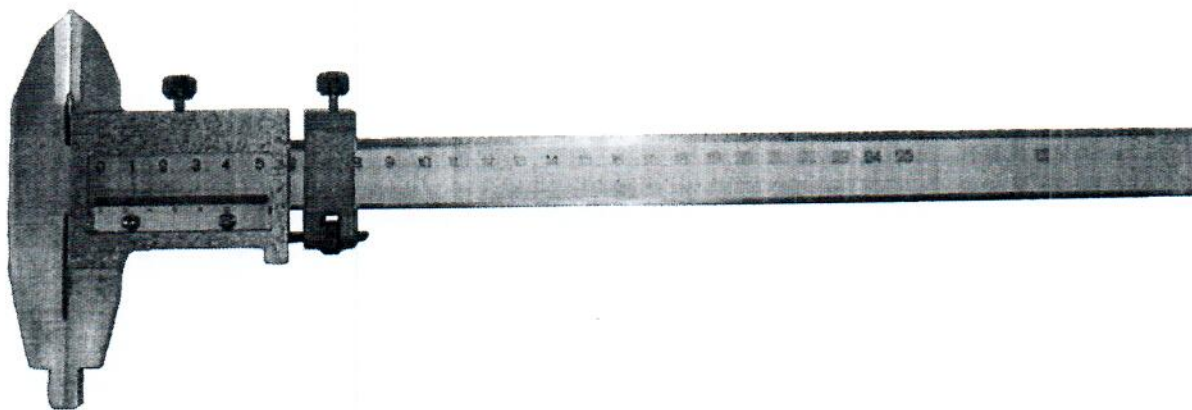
Внешний вид штангенциркуля типа ШЦ-II
